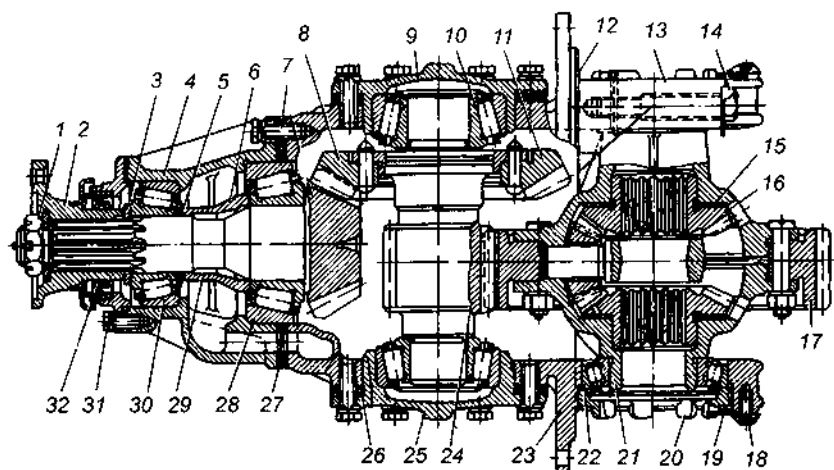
Редуктор и главная двухступенчатая передача: 1 — гайка фланца; 2 — фланец; 3 — регулировочная шайба; 4 — шайба; 5 — стакан подшипников; 6, 7, 14, 31 — болты; 8 — ведущее коническое зубчатое колесо; 9 — крышка; 10 — подшипник промежуточного вала; 11 — ведомое коническое зубчатое колесо; 12, 25 — крышки подшипников промежуточного вала; 13 — крышка; 15 — опорная шайба; 16 — зубчатое колесо полуоси; 17, 24 — ведомое и ведущее зубчатые колеса соответственно; 18 — болт стопора; 19 — стопор; 20 — регулировочная гайка; 21 — левая чашка; 22 — подшипник дифференциала; 23 — картер редуктора; 26, 27 — регулировочные прокладки; 28, 30 — подшипники вала ведущего конического зубчатого колеса; 29 — распорная втулка; 32 — манжета
